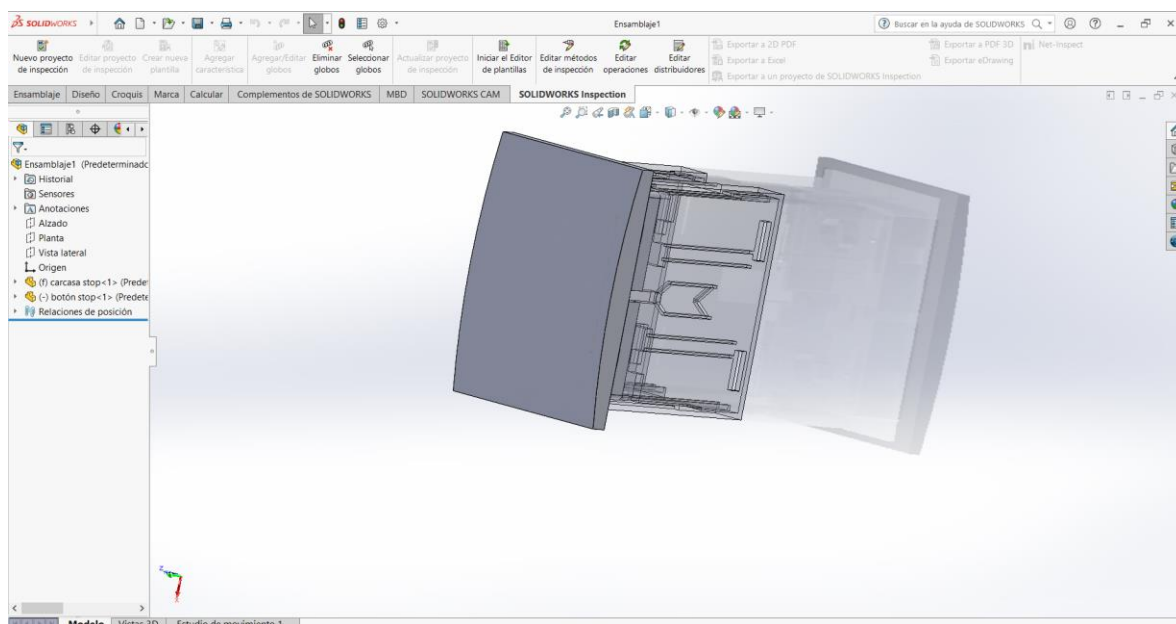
Diseño programa de moldeo Botón de Parqueo
